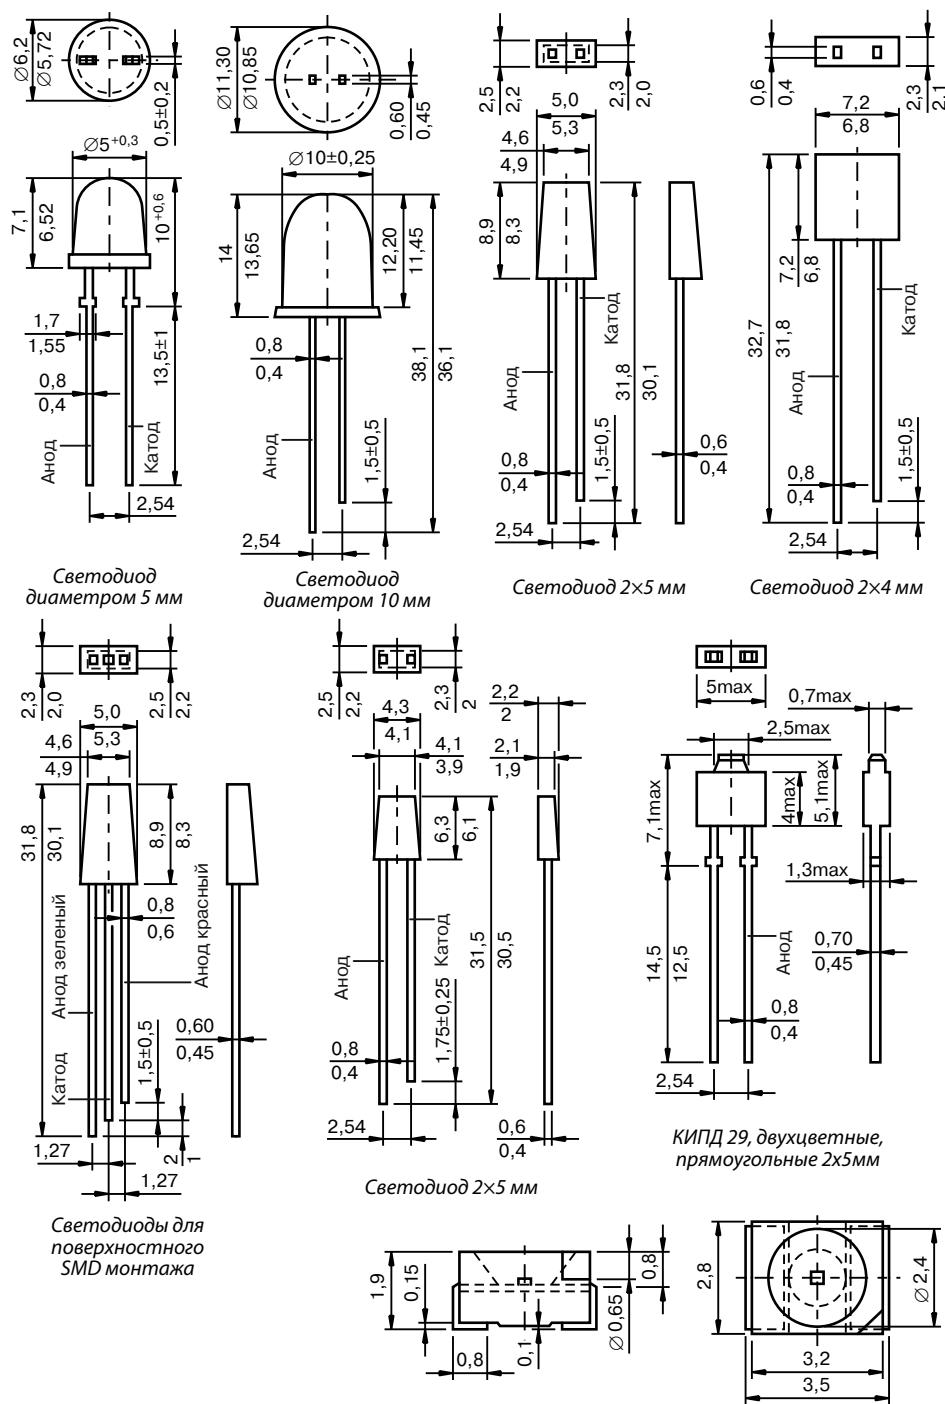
Внешний вид и габаритные размеры светодиодов
